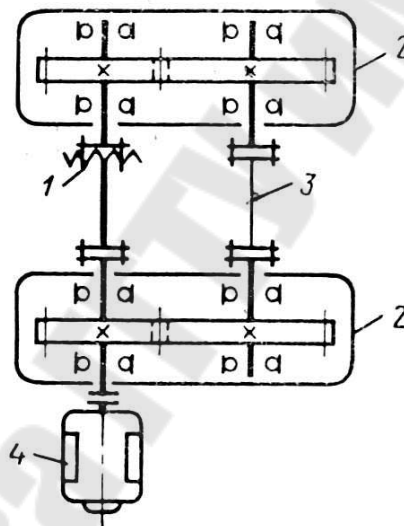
Замкнутый контур для испытания зубчатых агрегатов:
